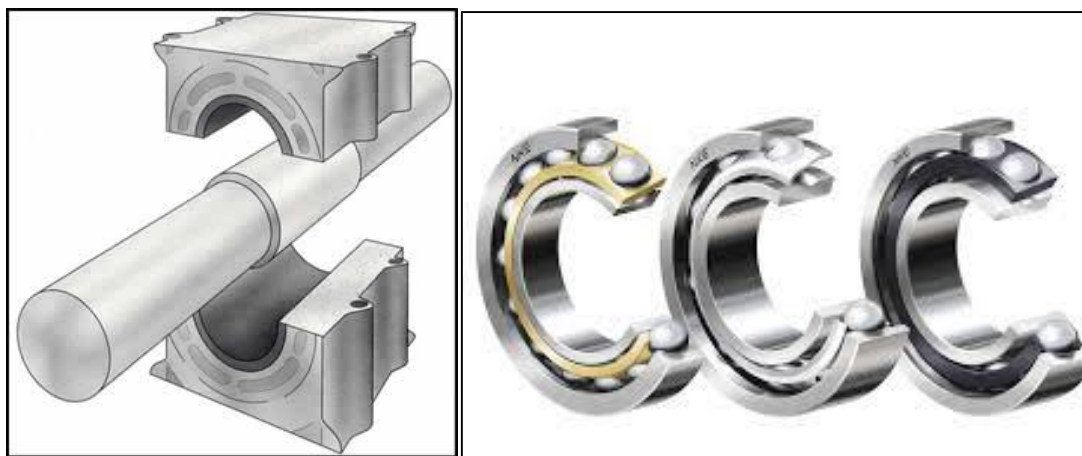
Cojinete de deslizamiento y cojinete de rodadura
